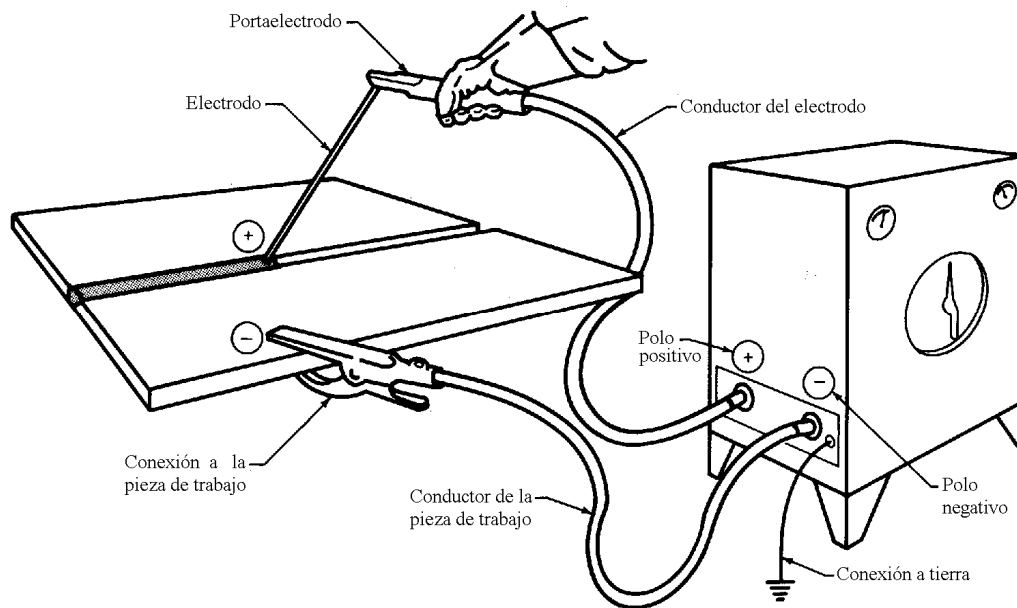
Equipo convencional para Soldadura por Arco Metálico Revestido (SMAW)
